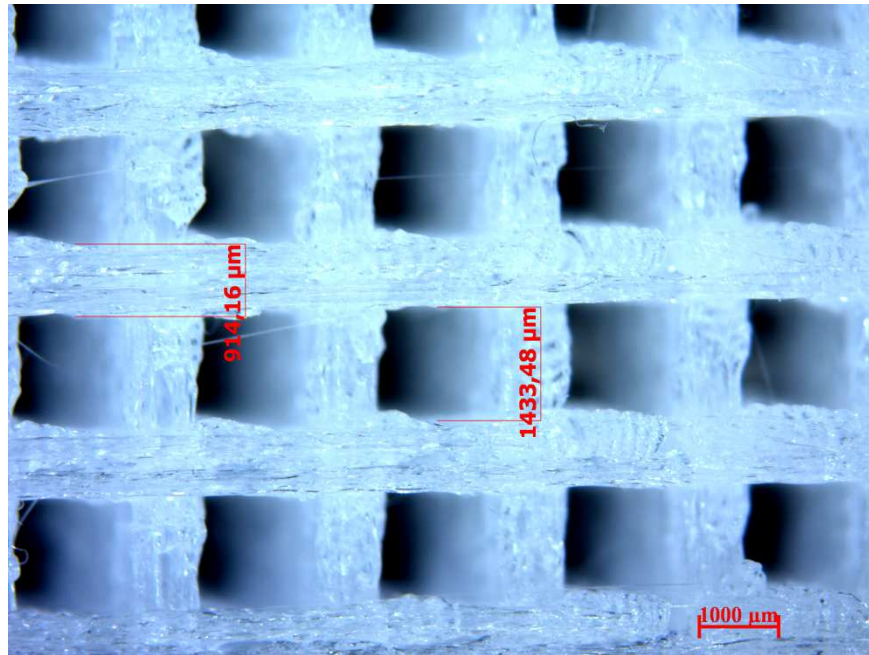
Scaffold in PLA creato dalla stampante 3D
